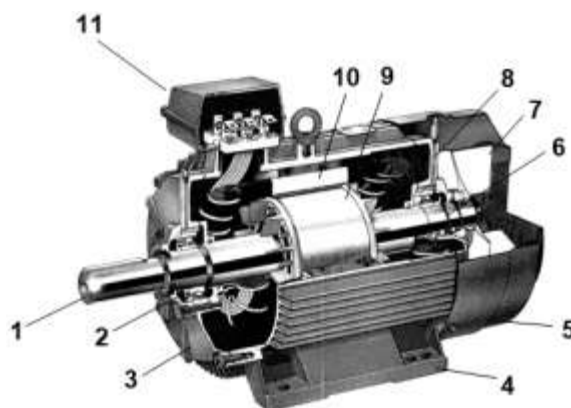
1 — вал; 2, 6 - підшипники; 3, 8 — підшипникові щити; 4 — лапи; 5 — кожух вентилятора; 7 — крильчатка вентилятора; 9 — короткозамкнутий ротор; 10 — статор; 11 — коробка виводів.
